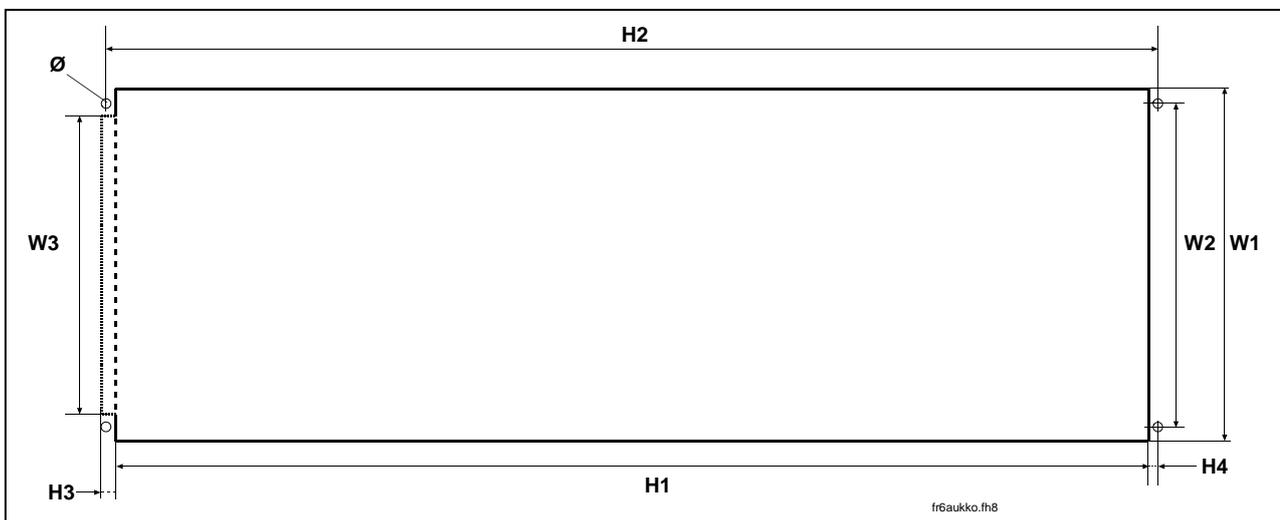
Ouverture pour le montage traversant sur bride, tailles FR4 et FR6
